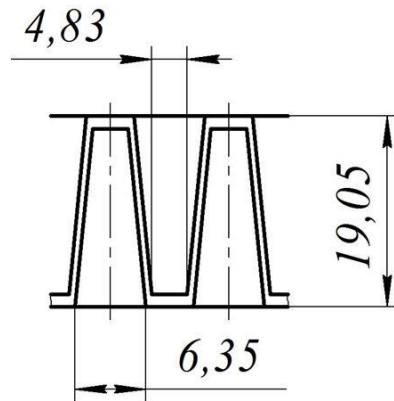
Пластинчато-ребриста поверхня ГЛР-3
